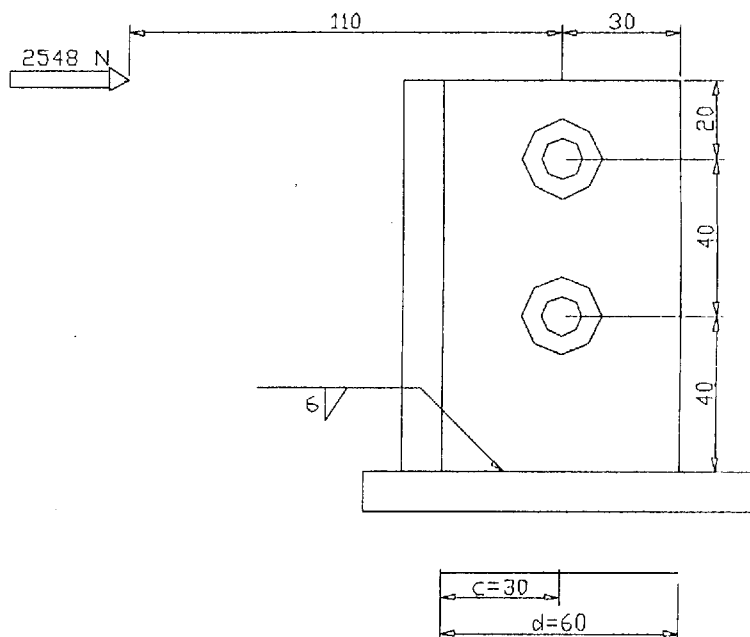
Dimensiones para el Cálculo de la Soldadura.
